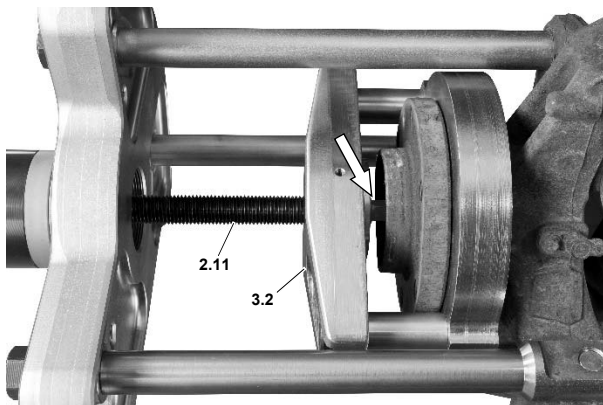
Zug-/Druckspindel in Brücke einschrauben.
